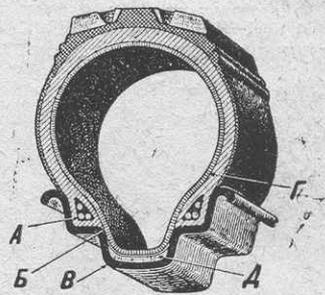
Разрез безбортовой покрышки на углубленном обode.
